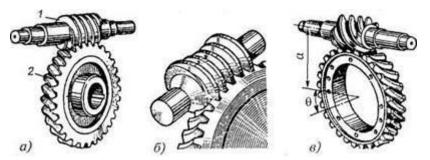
Червячные передачи: 1 — червяк; 2— червячное колесо
